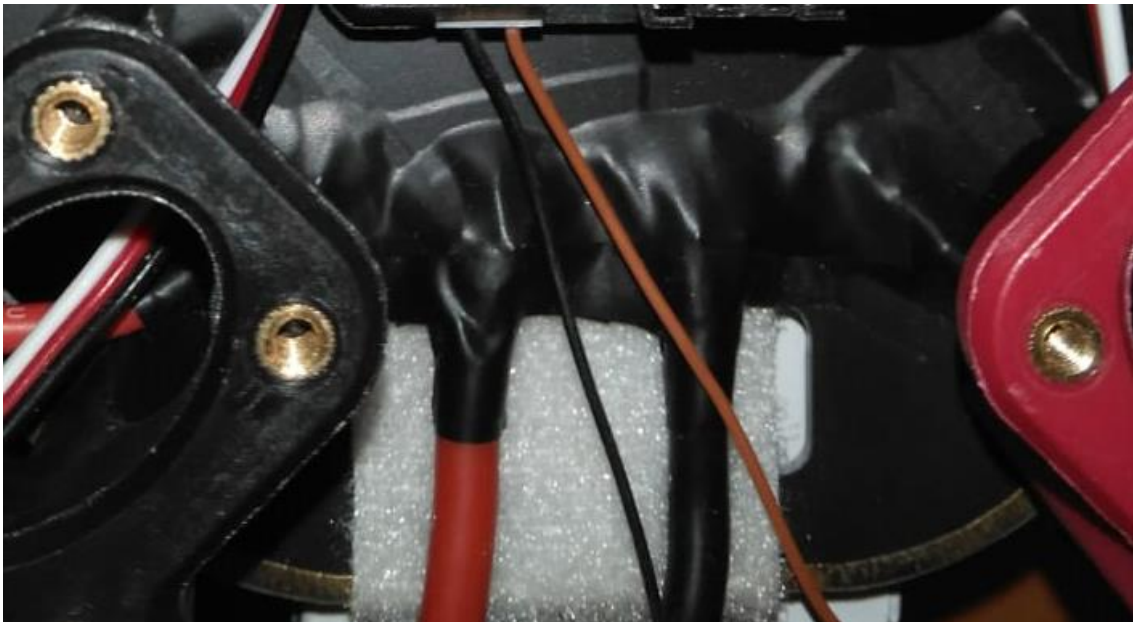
Muestra de la soldadura en la PDB
